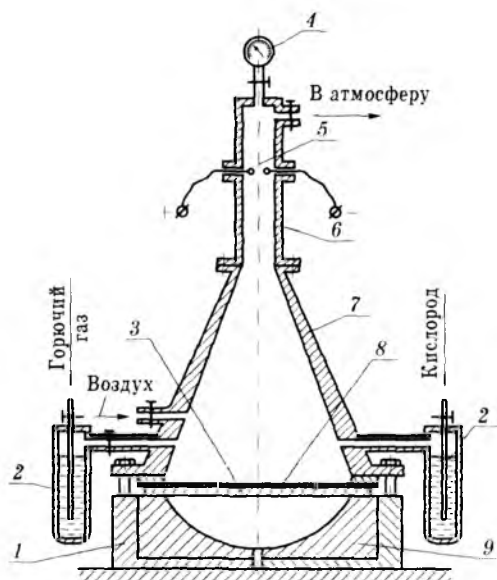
Схема листовой штамповки взрывом горючей смеси газов:
